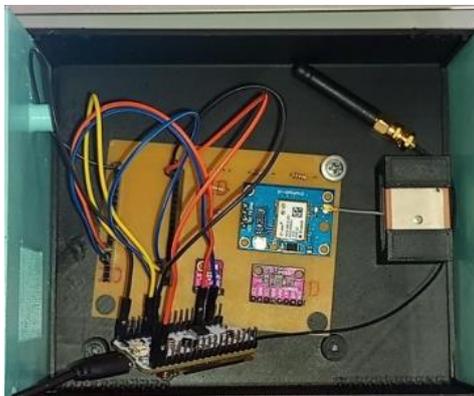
Placa com os componentes soldados e fixados em um chassi feito em impressora 3D
